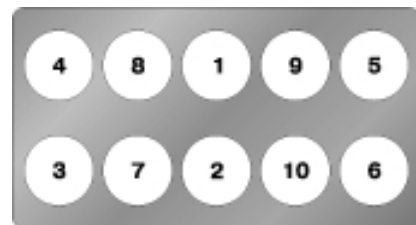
Порядок отворачивания и затягивания болтов и гаек крепления крышек подшипников распределительного вала двигателя F3R 272
